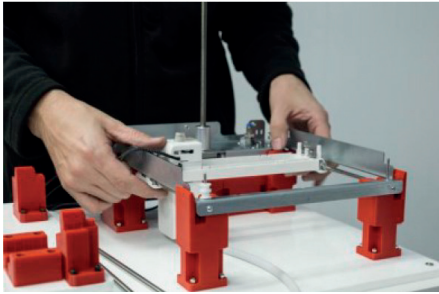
Utillaje de producción para línea de montaje fabricado por Alpha mediante la técnica FDM
